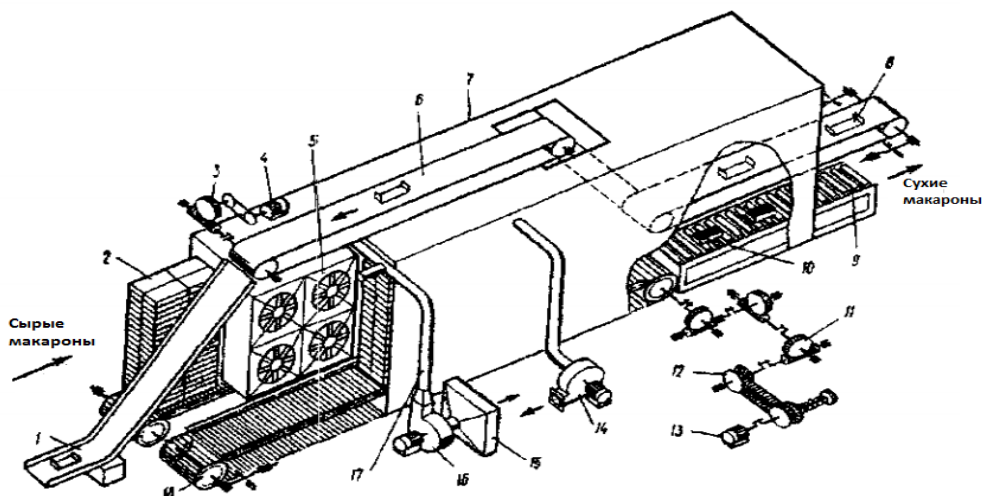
Стрічкова сушарка марки ЛС-2А
